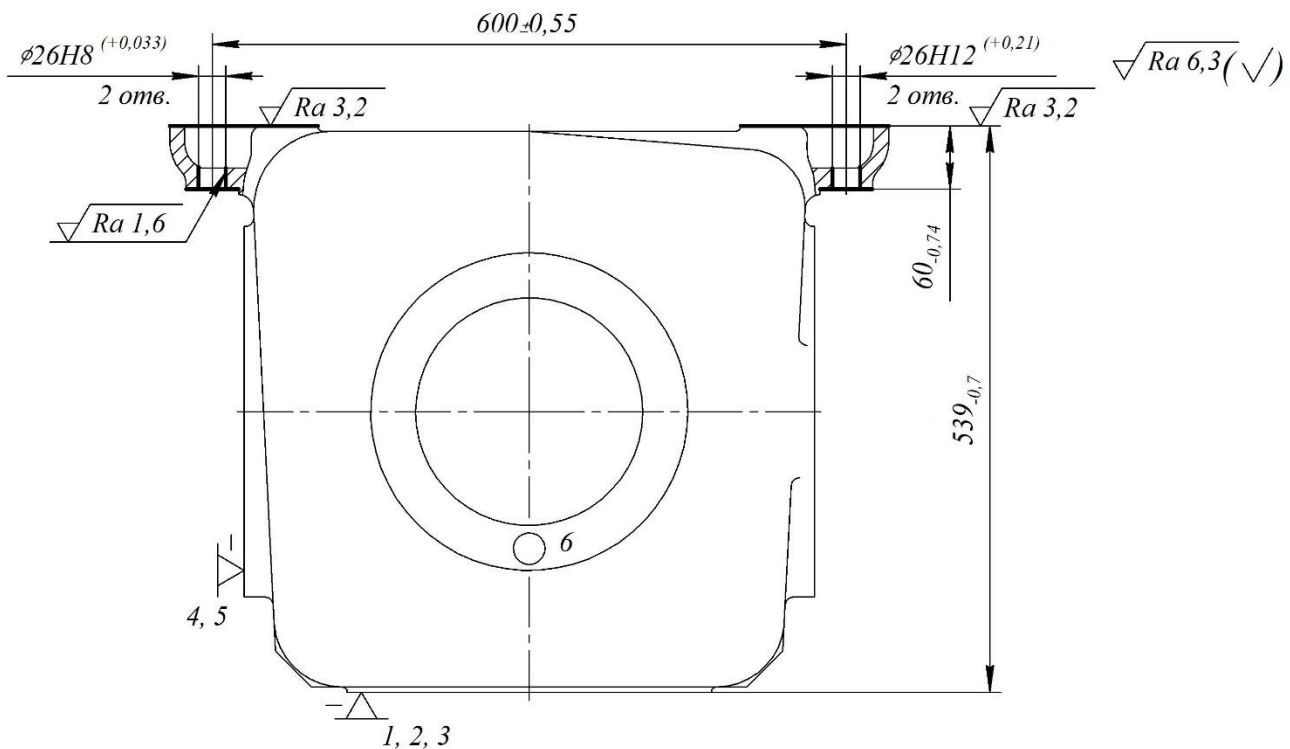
Схема базування заготовки на фрезерно-свердильній операції 015
